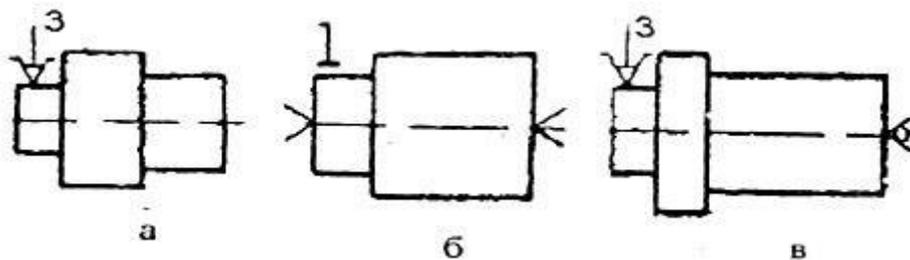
Способы установки заготовок на токарном станке: а – в патроне; б – в центрах; в – в патроне с подпором задним центро
